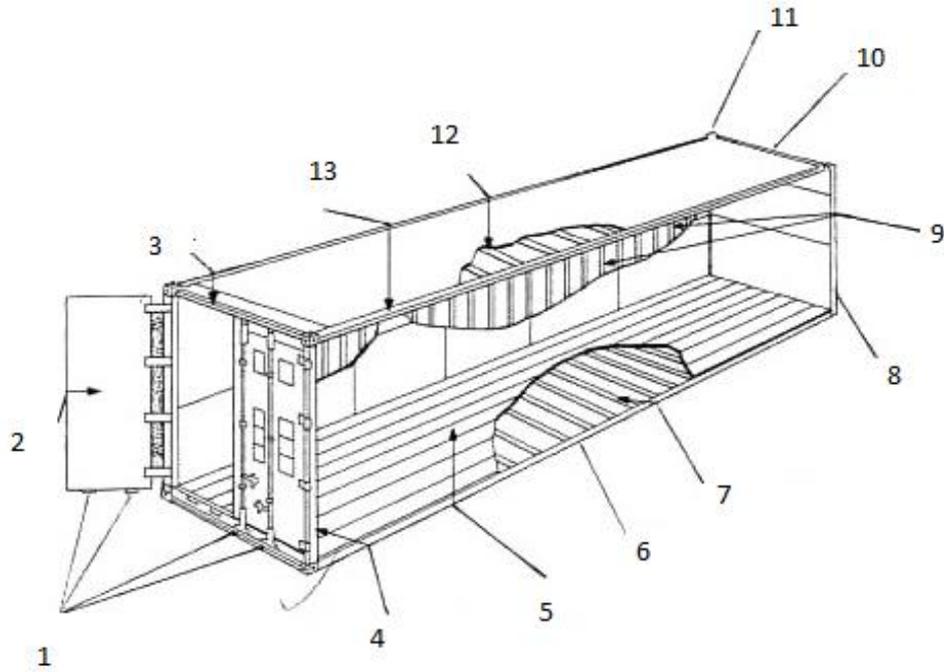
partes estructurales de un contenedor DRY-VAN
